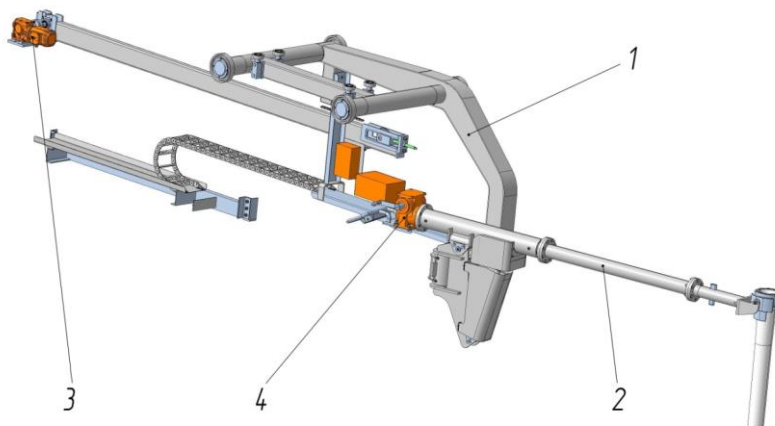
Пристрій для встановлення обертального захвату: 1 – несучий пристрій; 2 – стріла; 3 – механізм переміщення несучого пристрою; 4 – механізм для обертання стріли
